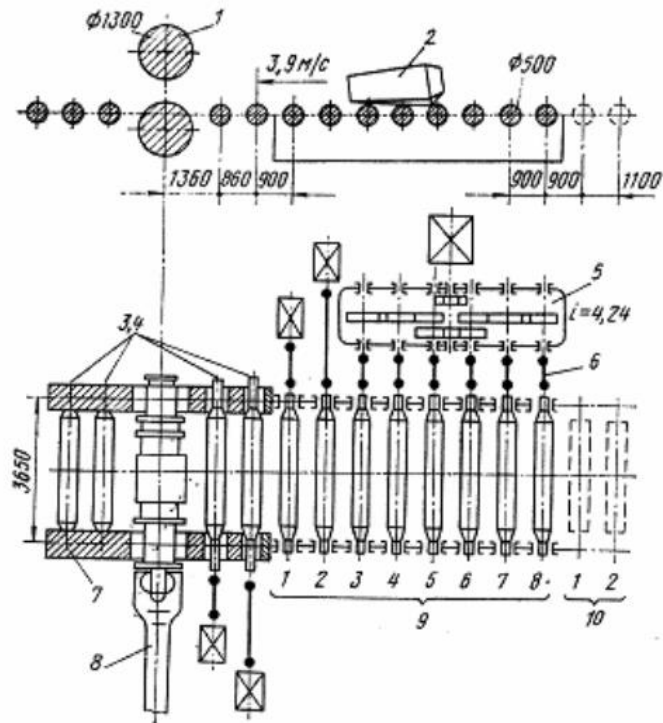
Робочий рольганг блюмінгу: 1 - валки; 2 - злиток; 3,4 - станинні ролики; 5 - редуктор; 6 - зубчасті шпинделі (муфти); 7 - станини робочої кліті; 8 - універсальні шпинделі від основних електродвигунів; 9 - робочий рольганг; 10 - розкочувальний рольганг
